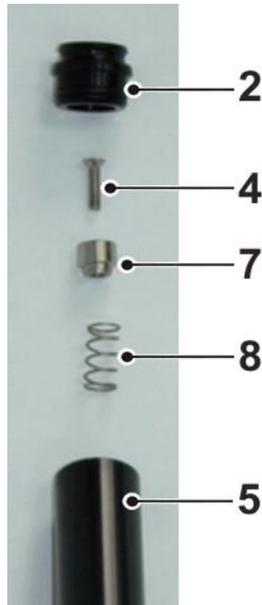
Rotoraufnahme mit Druckstück und Druckfeder
